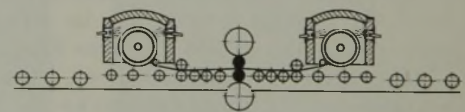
Steckel-Warmwalzwerk. Umkehrgerüst.
